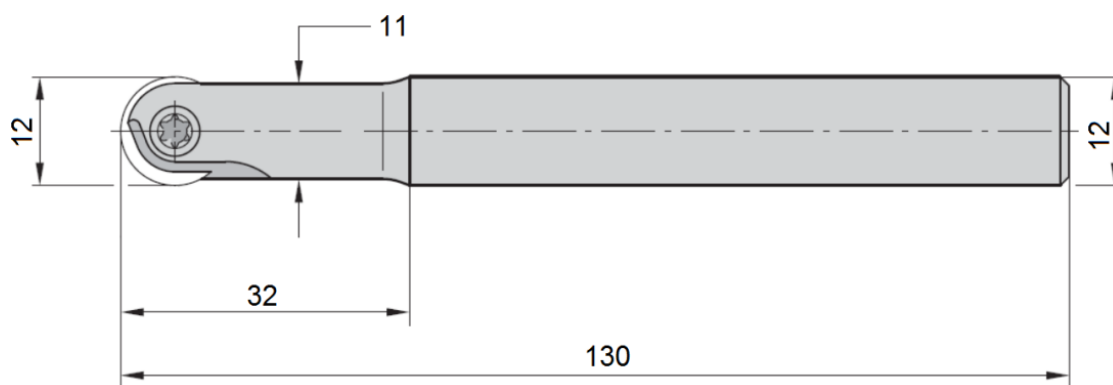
Plataforma de usinagem com inserto único intercambiável em metal duro utilizada na usinagem dos corpos de prova - CDPs
